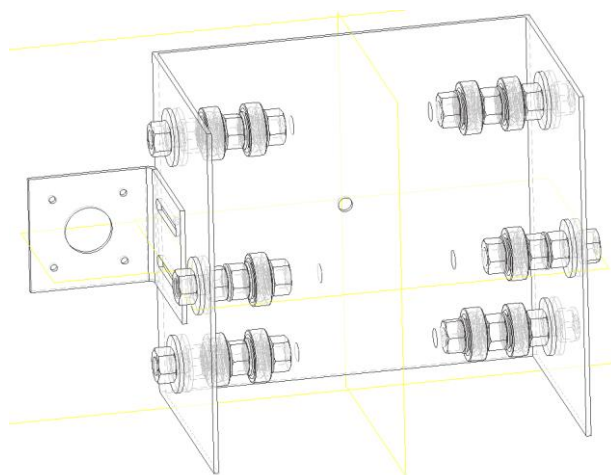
Rodamientos pieza deslizante. (Fuente propia).
